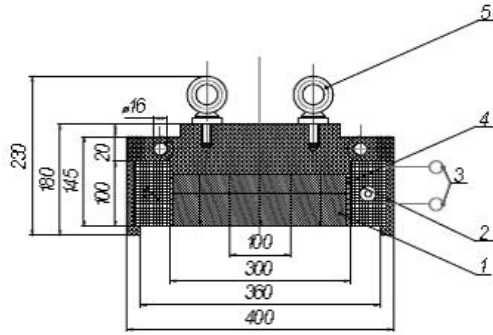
Конструкция КЖ блочного типа для установки над лентой конвейера шириной 400 мм: 1 — блоки ПМ; 2 — обмотка; 3 — выводы обмотки; 4 — рейки деревянные, фиксирующие обмотки и магнитные плиты; 5 — рым-болты для подъема КЖ
